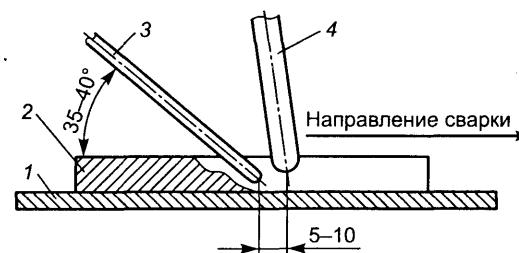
Схема расположения угольного электрода и присадочного прутка при сварке алюминия:
